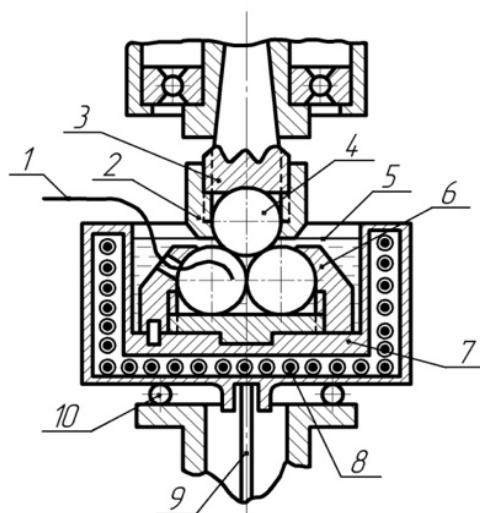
Схема узла трения машины КТ-2: 1 – термопара; 2 – накидная гайка; 3 – конус шпинделя; 4 – шарик; 5 – верхний уровень масла; 6 – оправка; 7 – корпус нагревателя; 8 – спираль нагревателя; 9 – торсион, 10 – опорный подшипник.
